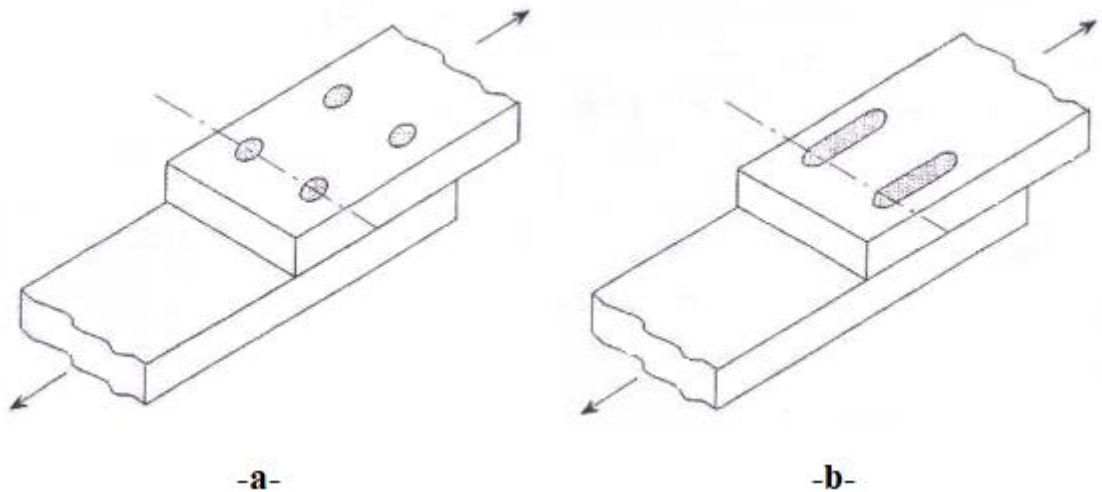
Soudure en bouchon et en entaille
